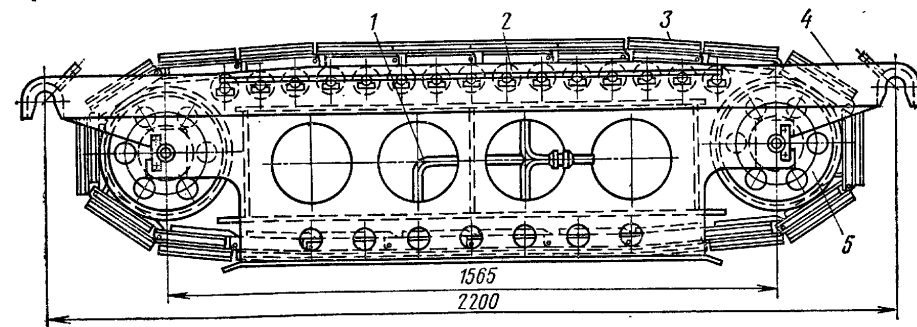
Гусеничный башмак для сварки наружных продольных швов труб:
